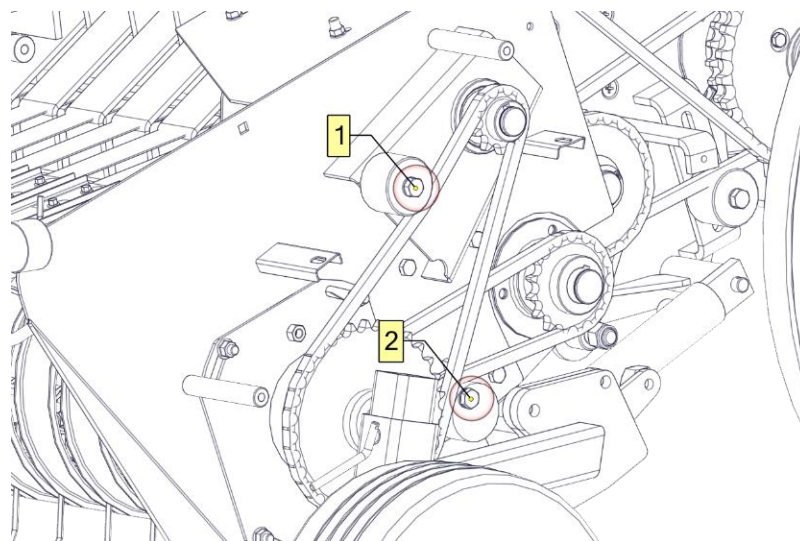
Регулировка натяжения цепей пресс-подборщика.
